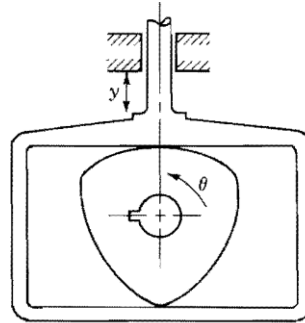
Leva de Anchura Constante con seguidor de movimiento alternativo y cara plana.
